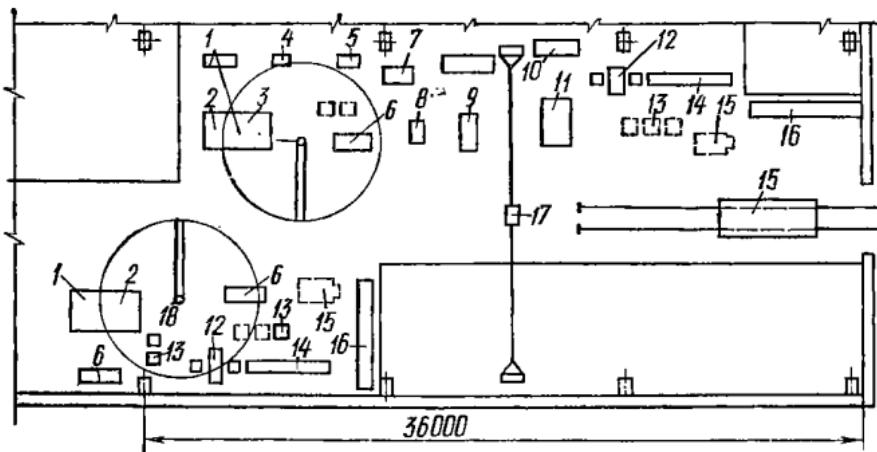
Механизированный участок по изготовлению соединительных деталей и узлов пластмассовых трубопроводов:
